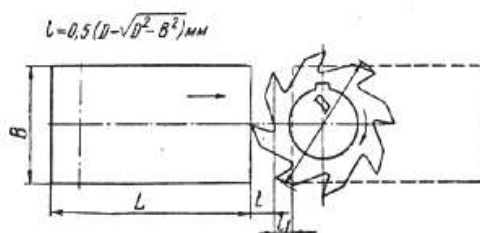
Врезание и перебег торцовой фрезы при симметричном фрезеровании
